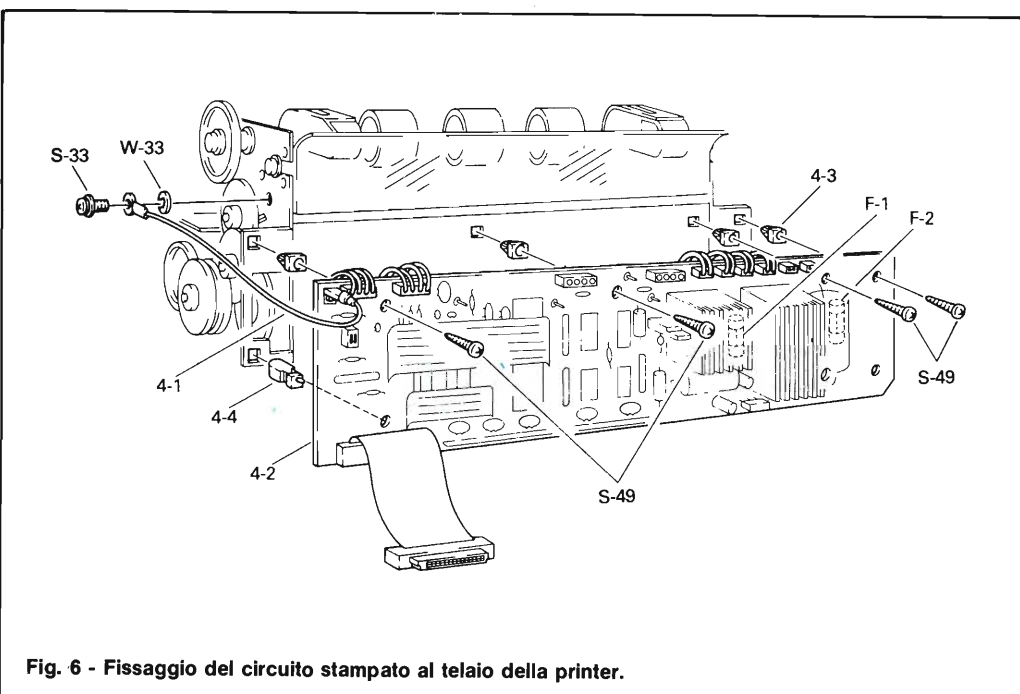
Fissaggio del circuito stampato al telaio della printer.
